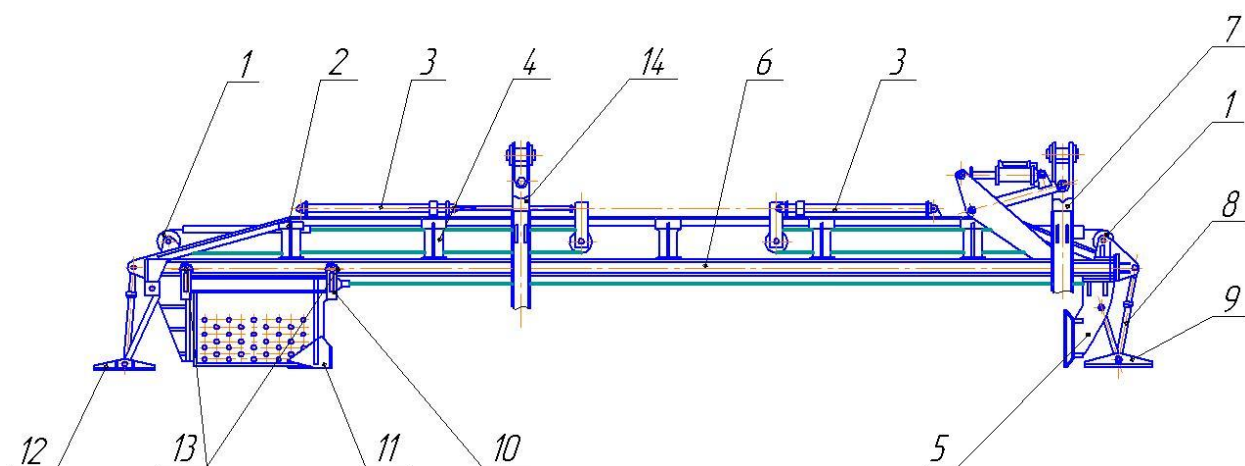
Рабочий орган с продольным движением ковша: 1, 2 – концевые блоки; 3 – гидроцилиндры передвижения ковша; 4 – рама рабочего оборудования; 5 – упорный щит; 6 – направляющие балки; 7, 14 – передний и задний телескопы стрелы; 8 – винтовая штанга; 9 – передняя подвижная опора; 10 – траверса; 11 – рабочий орган (ковш); 12 – задняя подвижная опора; 13 – роликовые опоры траверсы.
